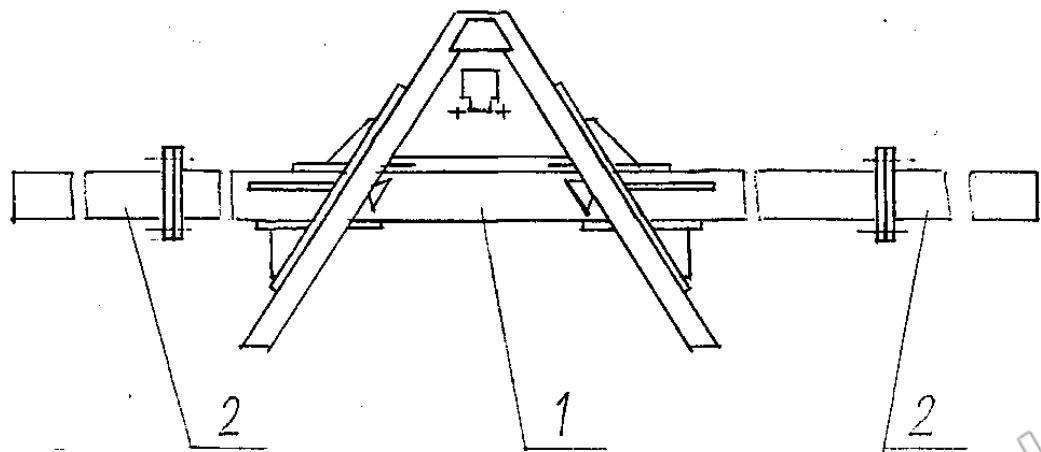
Культиватор-опрыскиватель универсальный КОУ-4/6
